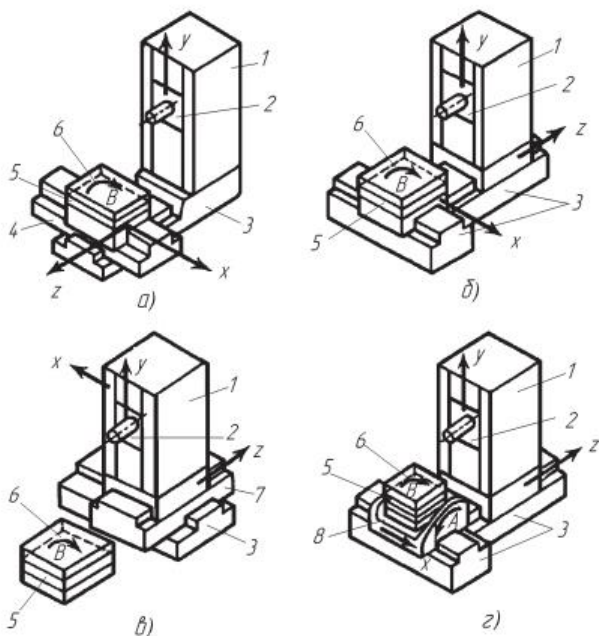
Горизонтальні ГВМ для обробки корпусних деталей
